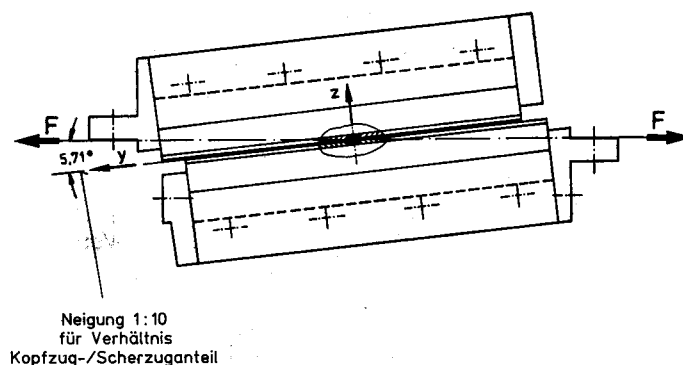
Punkgeschweißte Blechprobe.
